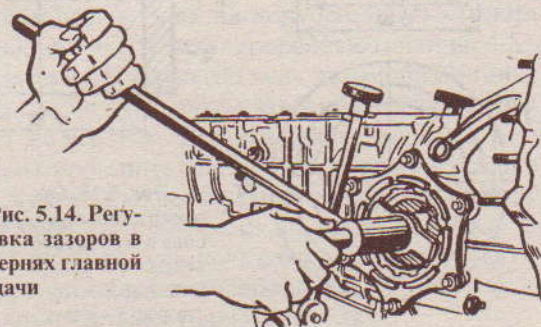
Регулировка зазоров в шестернях главной передачи
